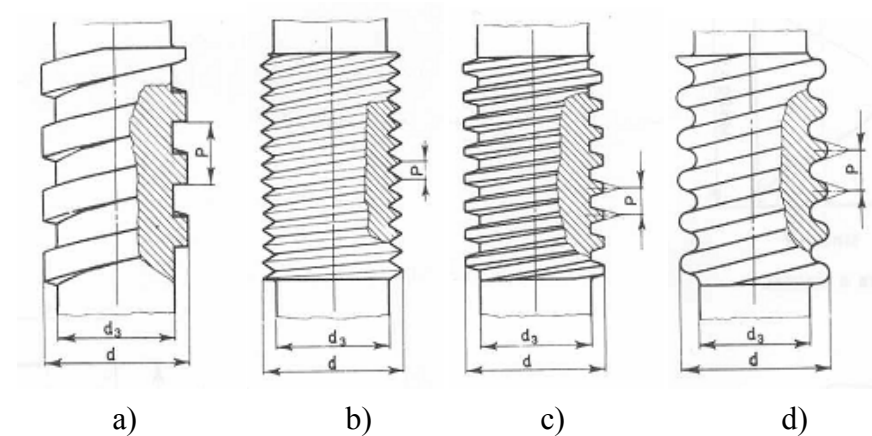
vite a profilo a) rettangolare, b) triangolare, c) trapezoidale e d) circolare.
